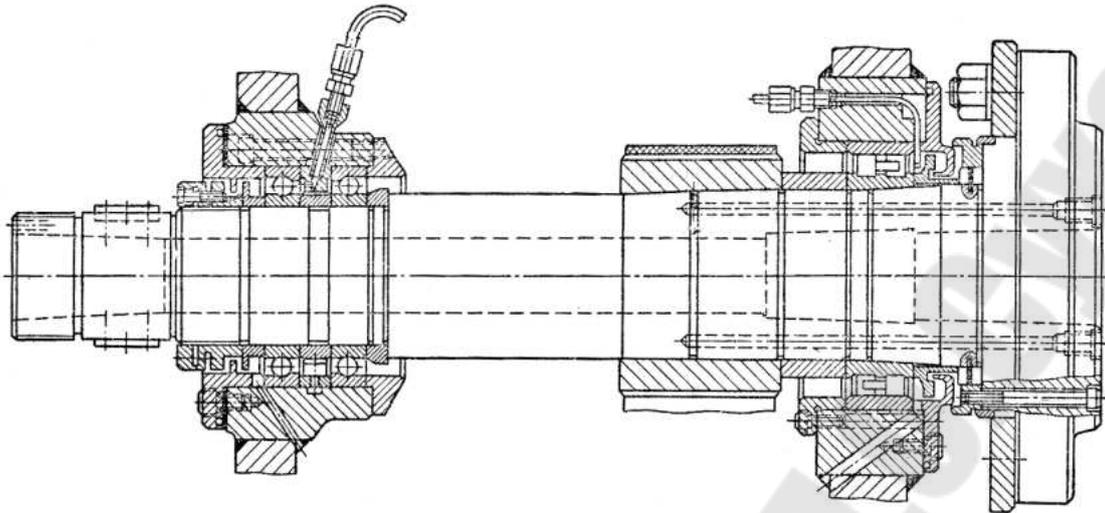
Шпиндельный узел быстроходного токарного станка
